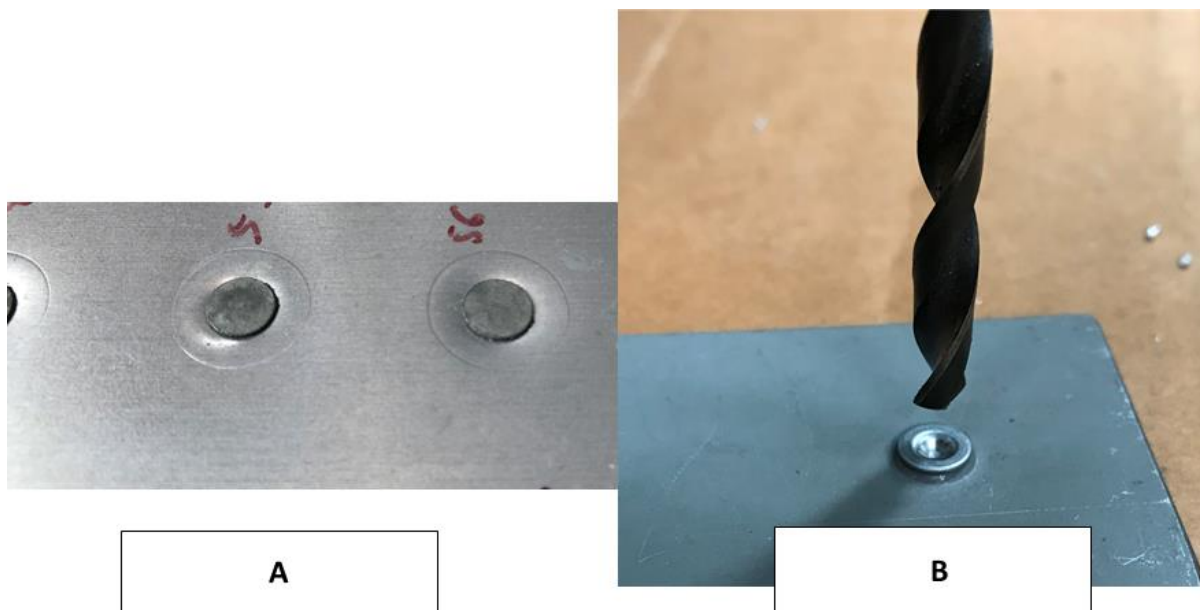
Taladrar una SPR desde la cara posterior (punta de remache), donde el acceso lo permita. A. Cabeza del remache - más difícil de taladrar, B. Punta del remache - más fácil de taladrar. Fuente: TWI
